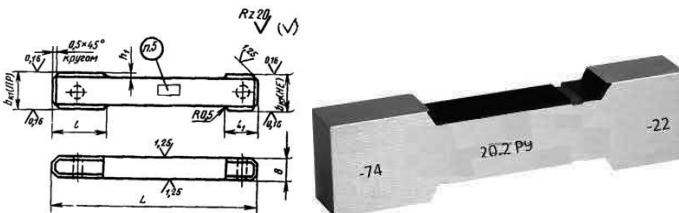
Калібр для контролю ширини шпонкового паза
